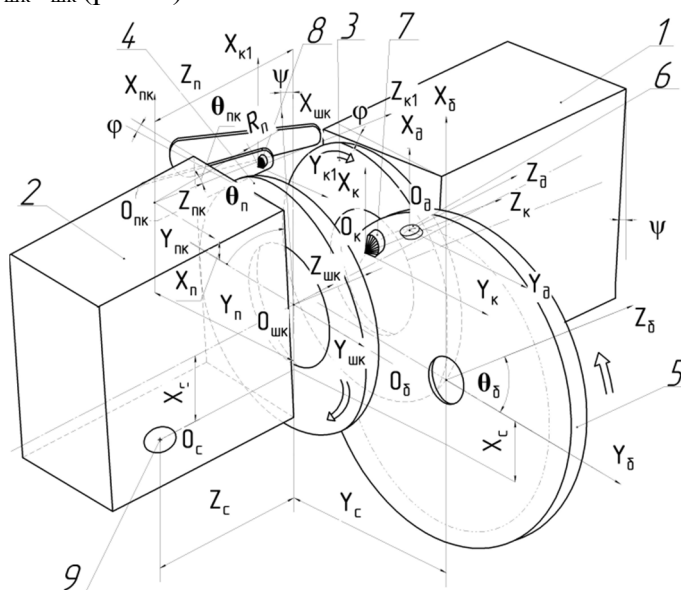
Розрахункова схема формоутворення циліндричних деталей з торцями різних діаметрів
